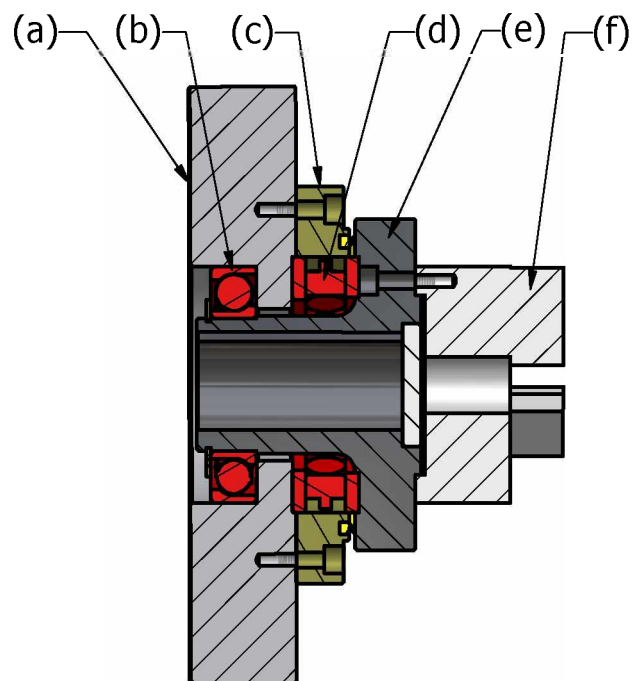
Schnittdarstellung der Elektromotoranbindung: Die Konstruktion setzt sich aus folgenden Teilen zusammen: (a) Gegenplatte motorseitig; (b) Radiallager; (c) Zentrierring mit Gummidichtung; (d) Axiallager; (e) Hohlwelle; (f) Dreibackenfutter.
